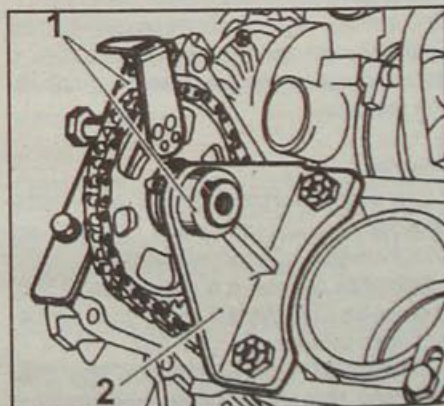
Фиксация звездочки распределительного вала приспособлением Mot. 589:
